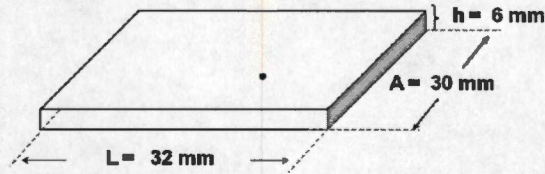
Esquema de dimensiones de la tapa de la celda de fluido (vista superior).
